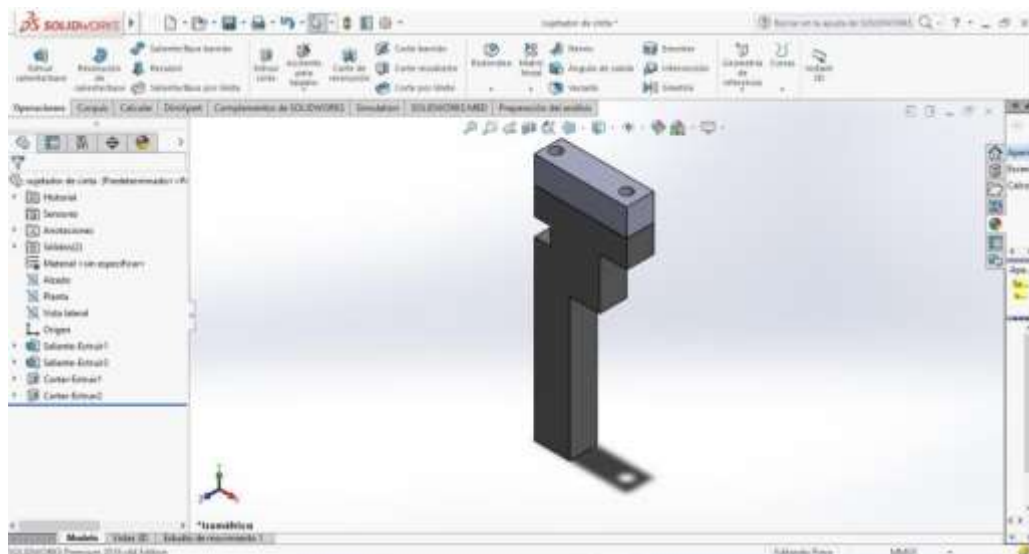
Sujetador de cintas o correa diseñado en SolidWorks.
